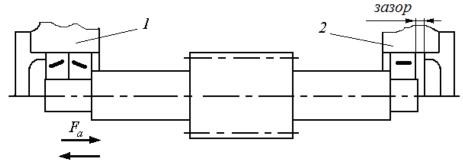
Установка червяка в опорах (опора 2 – плавающая)
